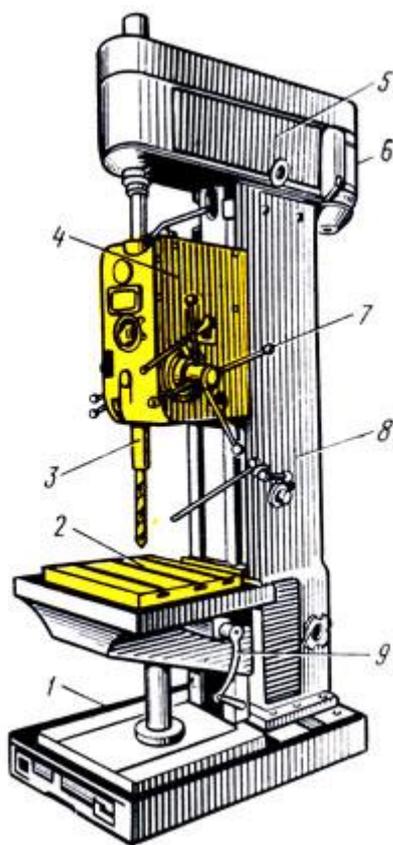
Вертикально-сверлильный станок 2А135: 1 - плита, 2 - стол, 3 - шпиндель, 4 - коробка подачи, 5 - шпиндельная головка 6 - электродвигатель, 7 - штурвал, 8 - станина, 9 - рукоятка
